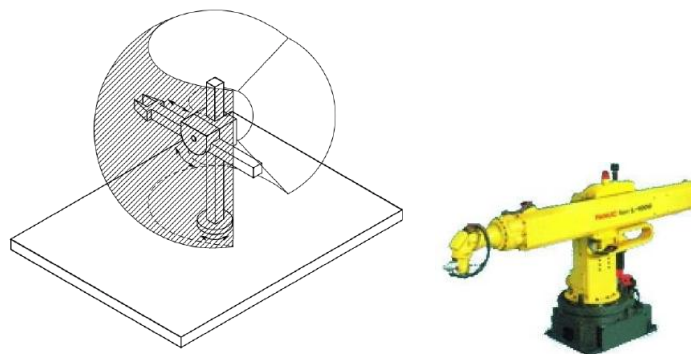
Manipulador Esférico (RRL): (a) desenho esquemático; (b) Robô polar industrial
